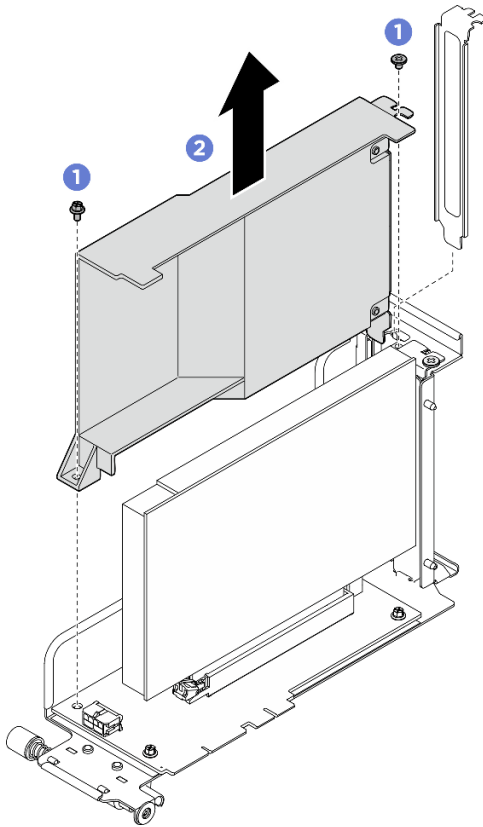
Entfernung der Luftführung für die PCIe-Adapterkarte
